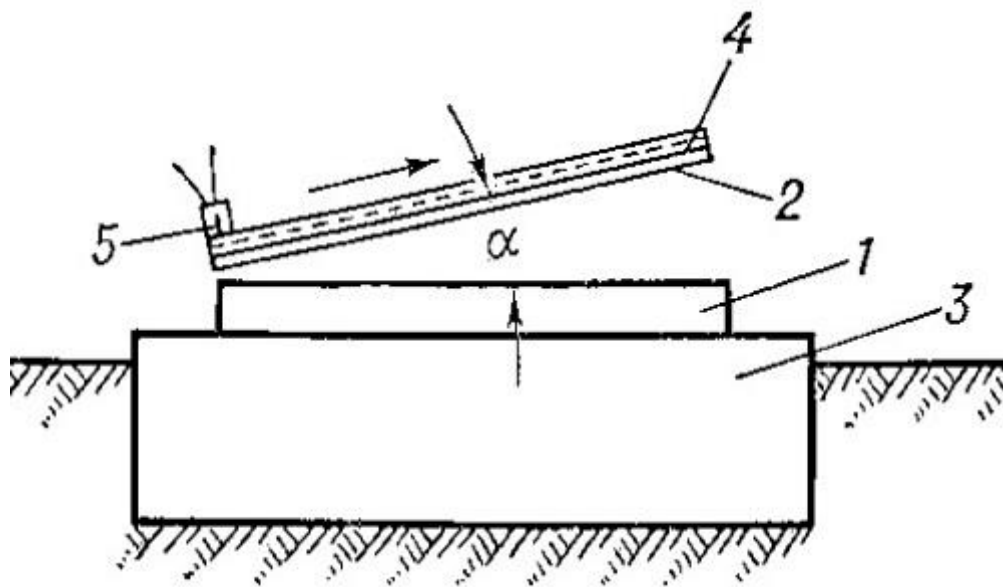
Схема взрывной сварки: 1 - неподвижная деталь (мишень), 2 - подвижная (метаемая) деталь, 3 - опорная плита, 4 - заряд, 5 – детонатор
